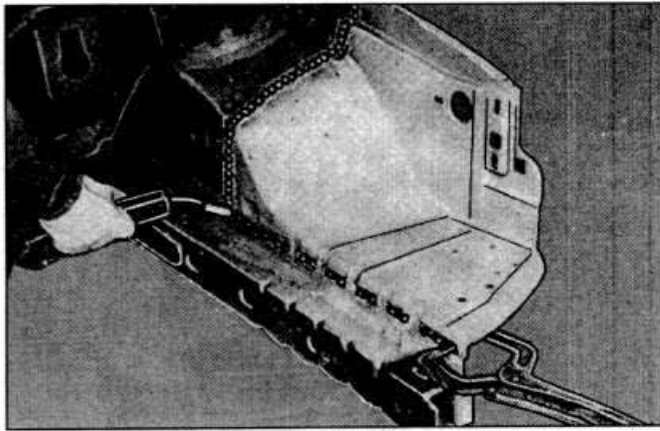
Приварка надколесного кожуха к лонжерону
